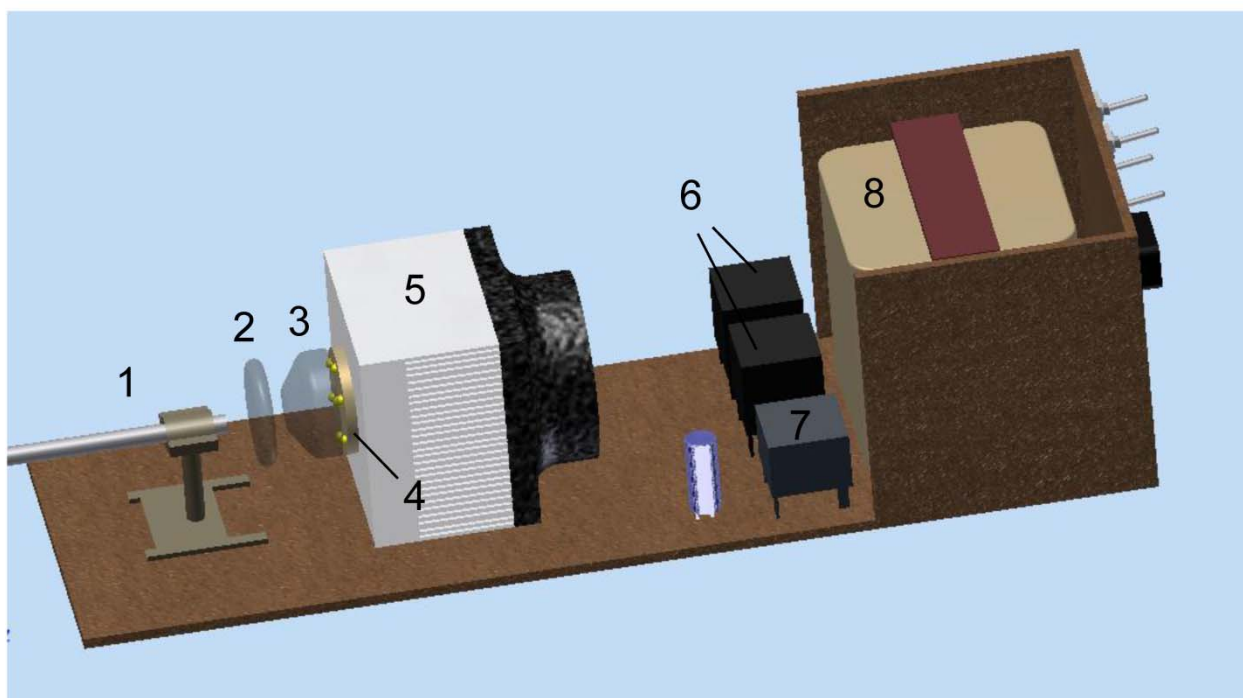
Конструкция осветителя. 1 – оптоволокну; 2 – нейтральный фильтр; 3 – коллектор; 4 – светодиодная сборка; 5 – радиатор с вентилятором; 6 – регуляторы тока; 7 – выпрямитель; 8 – трансформатор.
